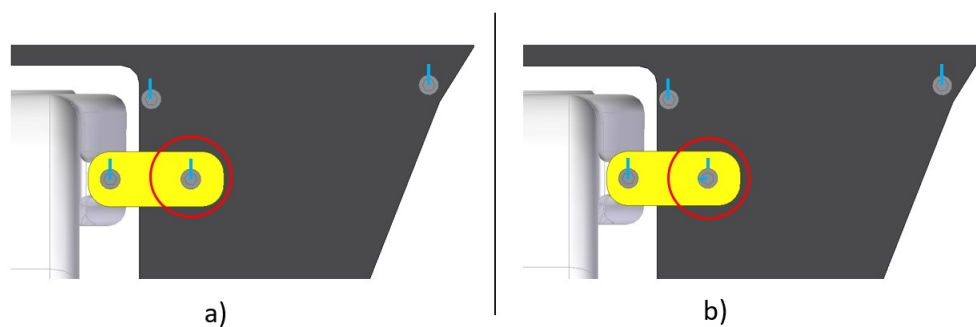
Ensamble tornillo con superficie de contacto a) Alineado b) Deaslineado
